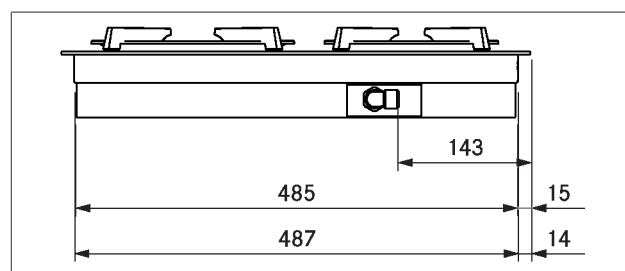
CKG apparatets dimensjoner sett fra siden
